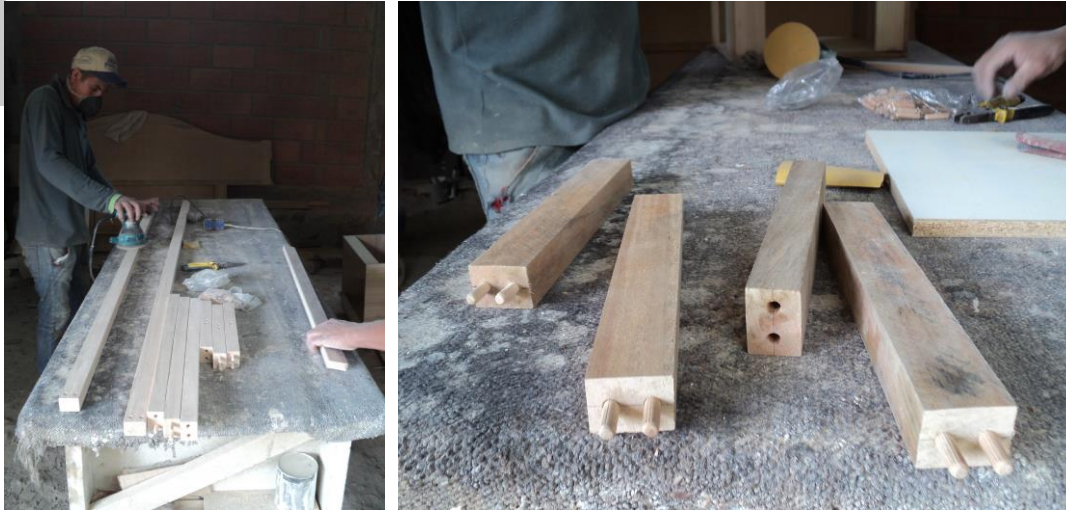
Lijan todas las tiras de madera, es decir las piezas que forman la estructura.
